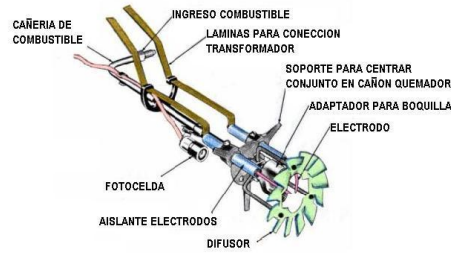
Conjunto quemador que controla el combustible, el aire y la ignición.
